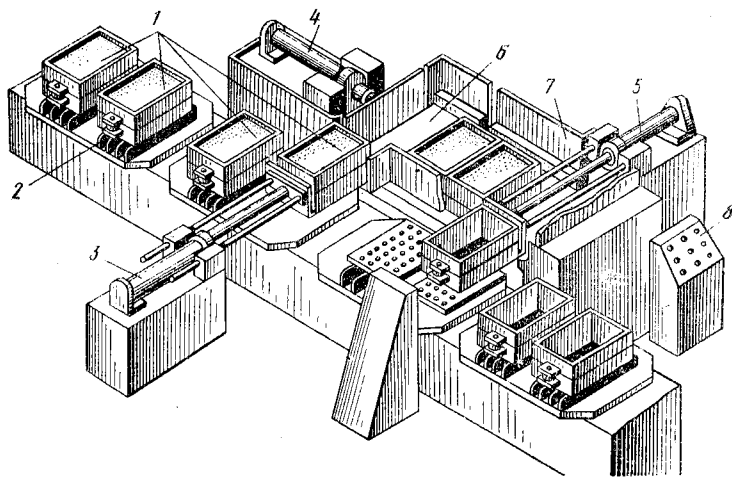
Схема устройства автоматической установки для выбивки песчаных форм:
